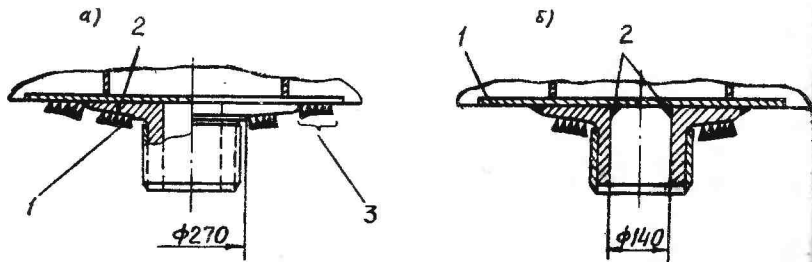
Усиление шкворневого узла кузова и схема расположения тензорезисторов. ▼ - вид тензорезистора сбоку;
